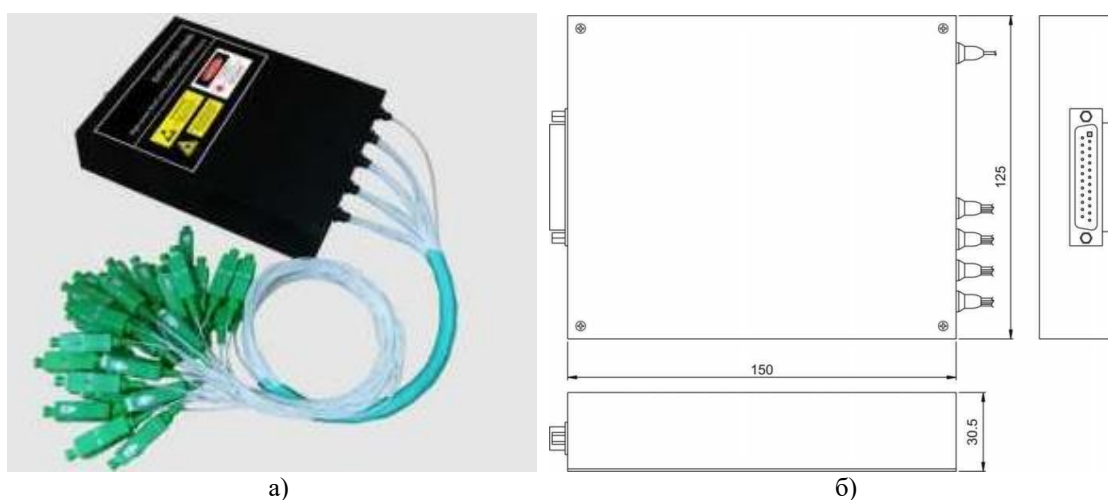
Внешний вид (а) и габаритный чертёж (б) конструкции EATV5400D.
